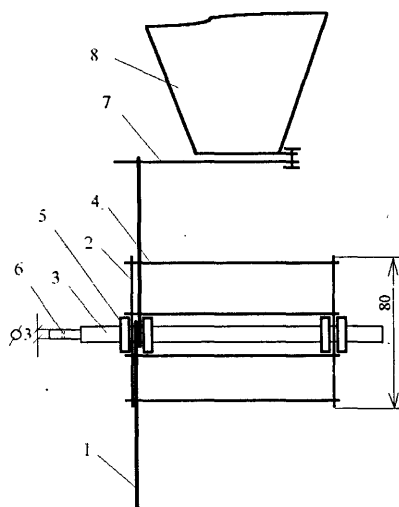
Барабан прикормки: 1 — спица; 2 — щечки; 3 — вал; 4 — распорки; 5 — гайки; 6 — отверстие под шплинт; 7 — задвижка; 8 — бункер
